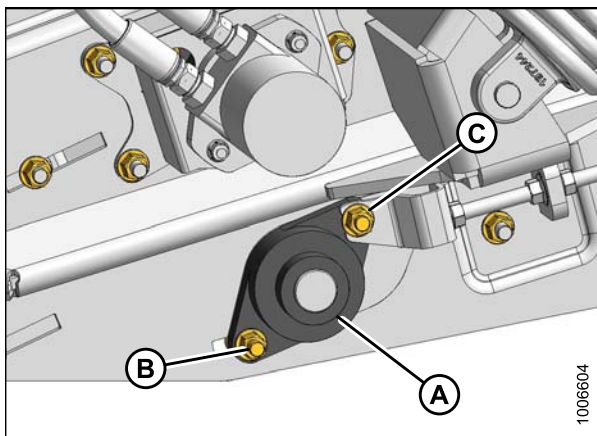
Подшипник натяжного ролика с левой стороны
